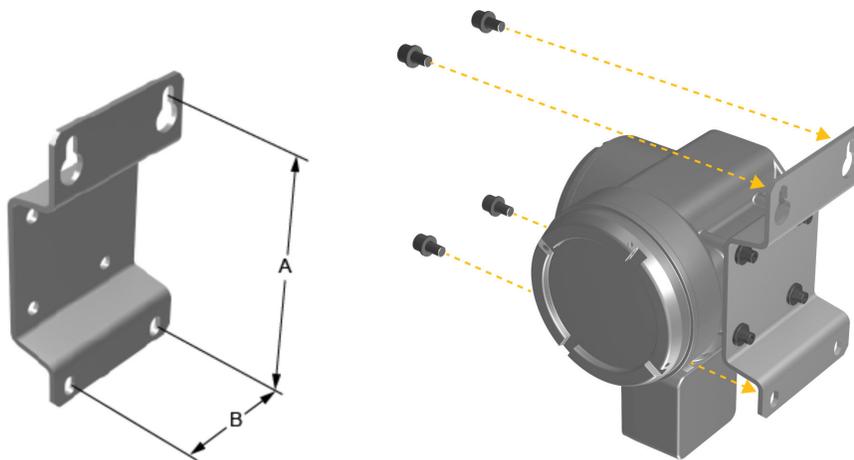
Кронштейн для настенного монтажа и размеры для преобразователя в алюминиевом корпусе
